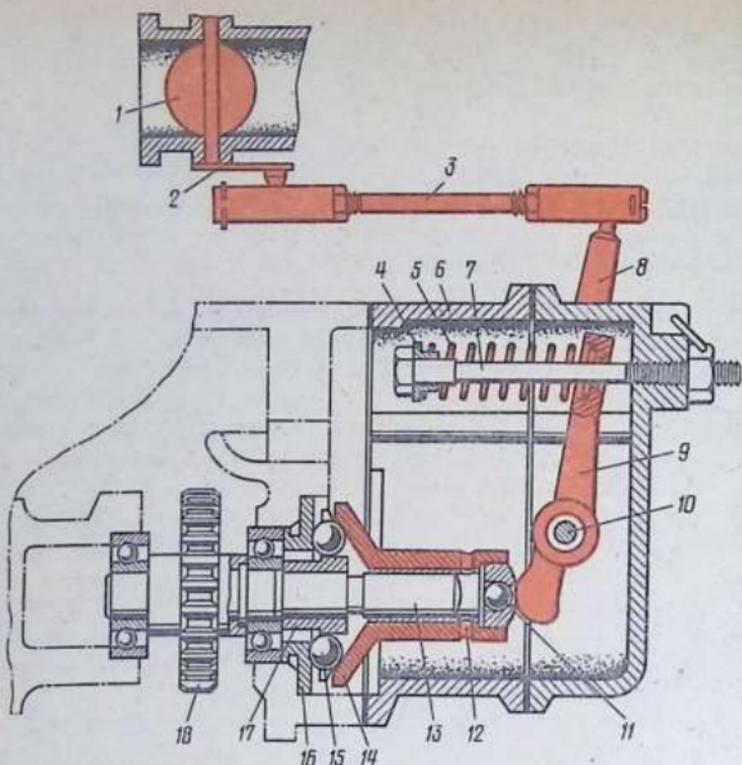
Однорежимный центробежный регулятор пускового двигателя П-10УД:
